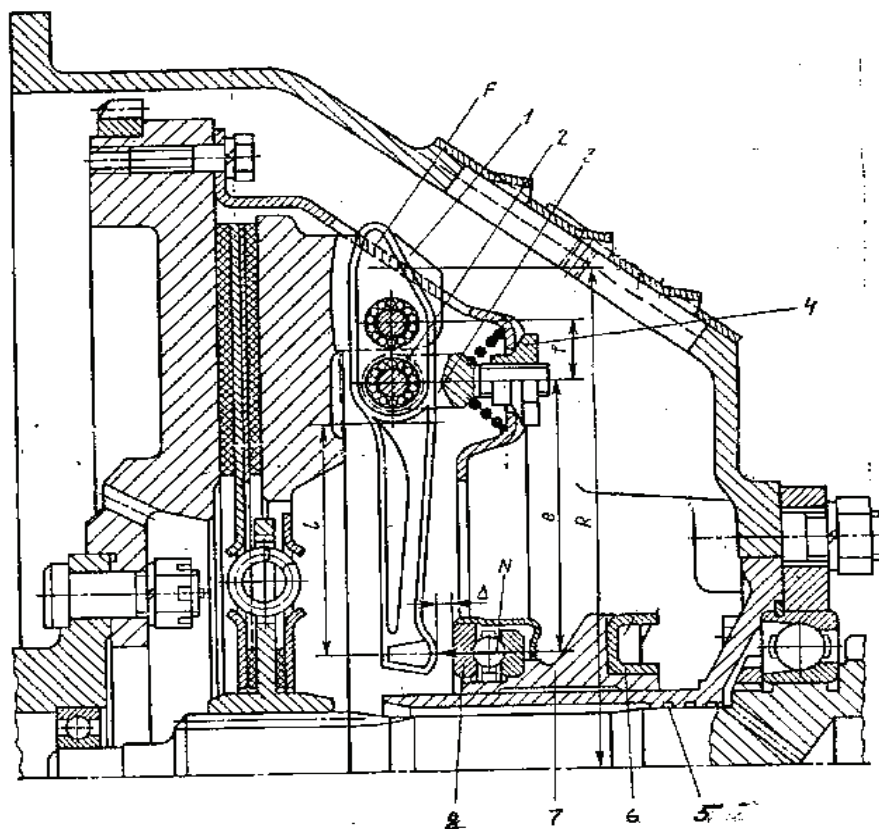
Расчетные размеры нажимного диска и рычага выключения: 1 – пружина; 2 – ось; 3 – опорная вилка; 4 – регулировочная гайка; 5 – передняя крышка коробки передач; 6 – вилка выключения; 7 – муфта выключения сцепления; 8 – упорный шарикоподшипник
